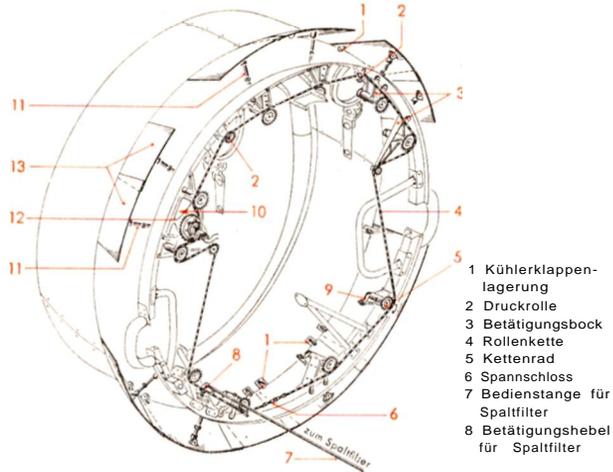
Motorspant I in Blechausführung mit Kühlerklappenbetätigung
